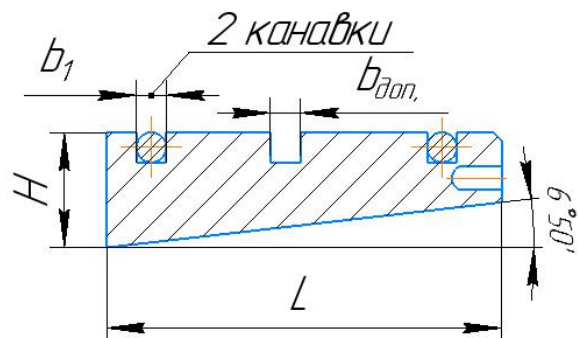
Эскиз кулачка оправки. Показана дополнительная канавка посередине для размещения разрезного кольца при обточке по месту
